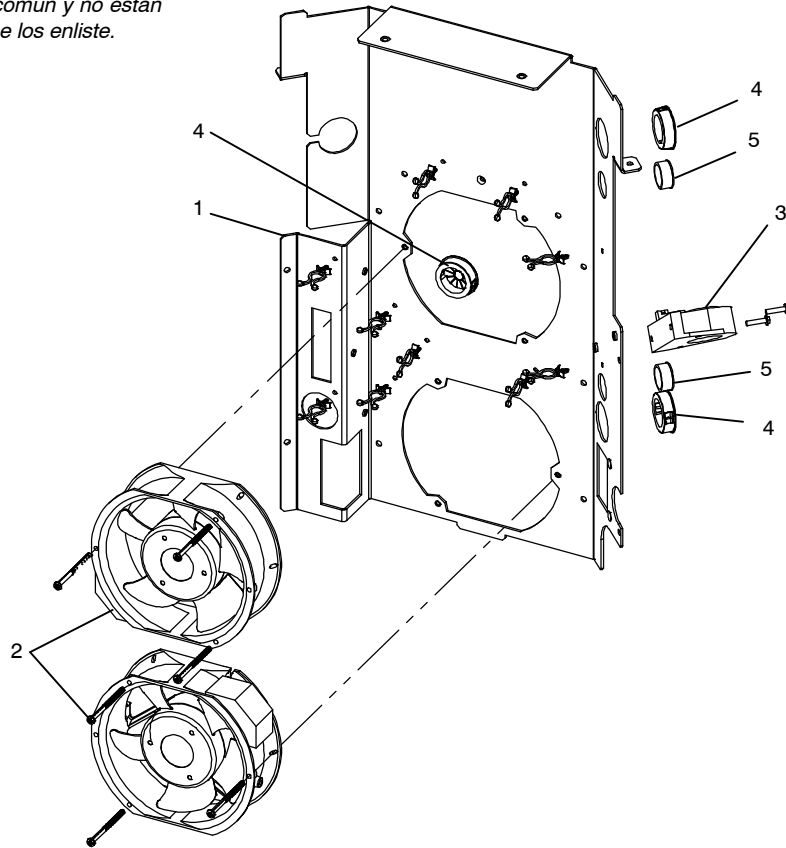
Conjunto Windtunnel izquierdo c/componentes
